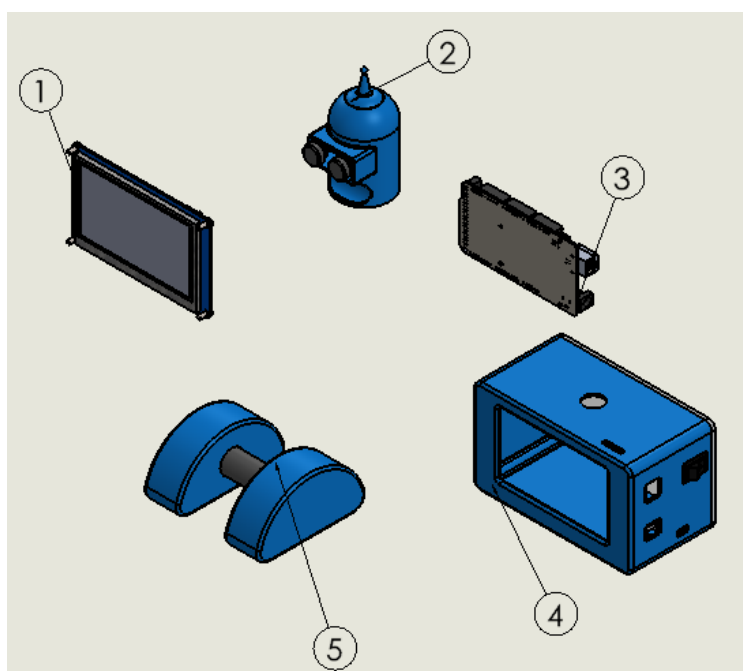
Vista isométrica explosionada de la primera alternativa de solución.
